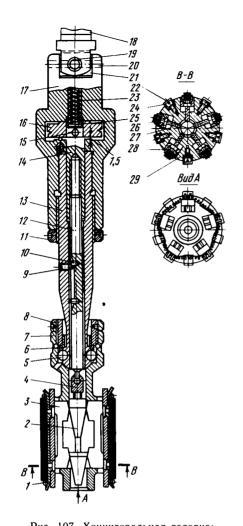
Хонинговальная головка: 1,23 — пружины; 2,18 — конусы; 3 — сухари; 4 — серьга; 5 — шарики; 6, 14 — втулки; 7 — гайка; 8, 11 — контргайки; 9, 10 — ограничительные винты; 12 — шток; 13 — штанга; 15 — штифт; 16 — маховичок настройки; 17 — патрон; 19, 20 — оси; 21 — головка шарнирного соединения; 22 — винт; 24 — направляющая; 25 — башмак; 26 — абразивный брусок; 27 — вкладыш; 28 — кассета; 29 — корпус
